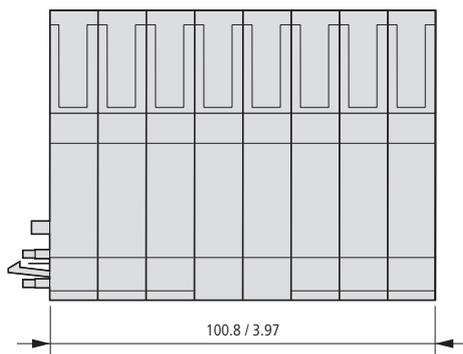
Rückansicht BL20-Modul komplett in Blockausführung
